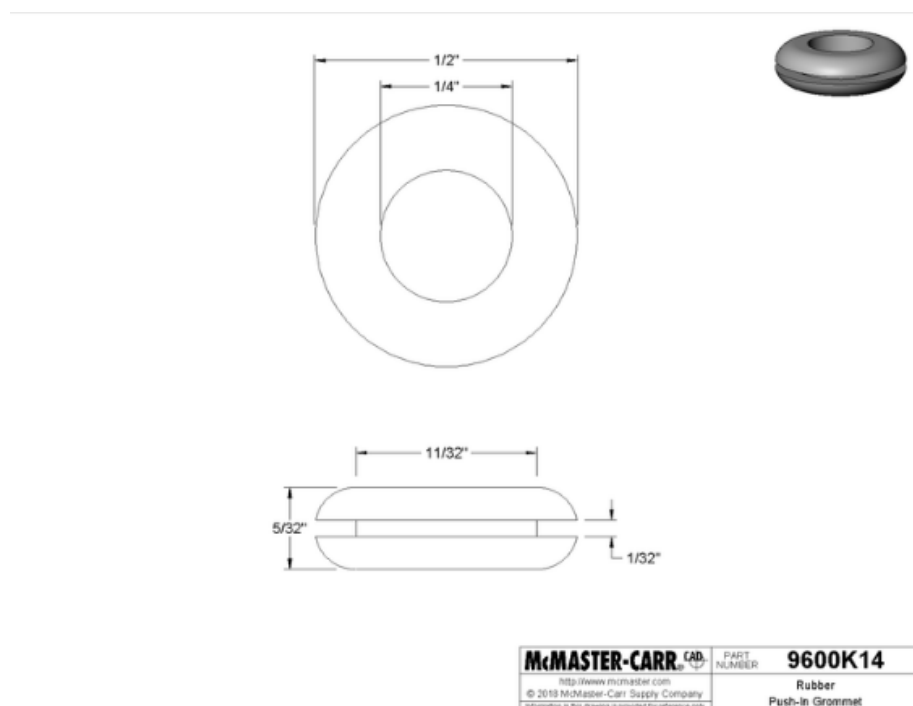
Plano técnico de empaque de caucho. Imagen tomada de: McMaster- CARR
